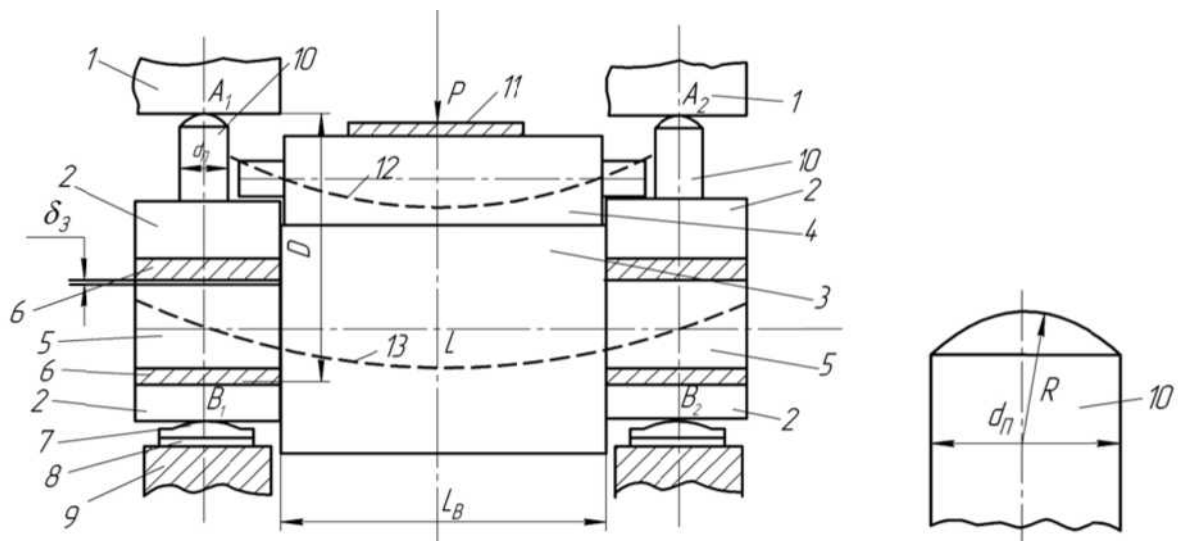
Комплект валків і подушок зі сферичними плунжерами: 1 - лапи верхніх подушок опорного валка; 2 - подушки нижнього опорного валка; 3 - нижній опорний валок; 4 - нижній робочий валок; 5 - шейку опорного валка; 6 - підшипник; 7 - прокладка з параболічною формою поверхні; 8 - прокладка; 9 - нижня поперечка станини; 10 - плунжер зі сферичною формою торця; 11 - штаба; 12 - лінія прогину робочого валка; 13 - лінія прогину опорного валка (P - сила прокатки; d_p - діаметр плунжера; R - радіус сферичної поверхні торця плунжера - $R = 200-500$ мм)
